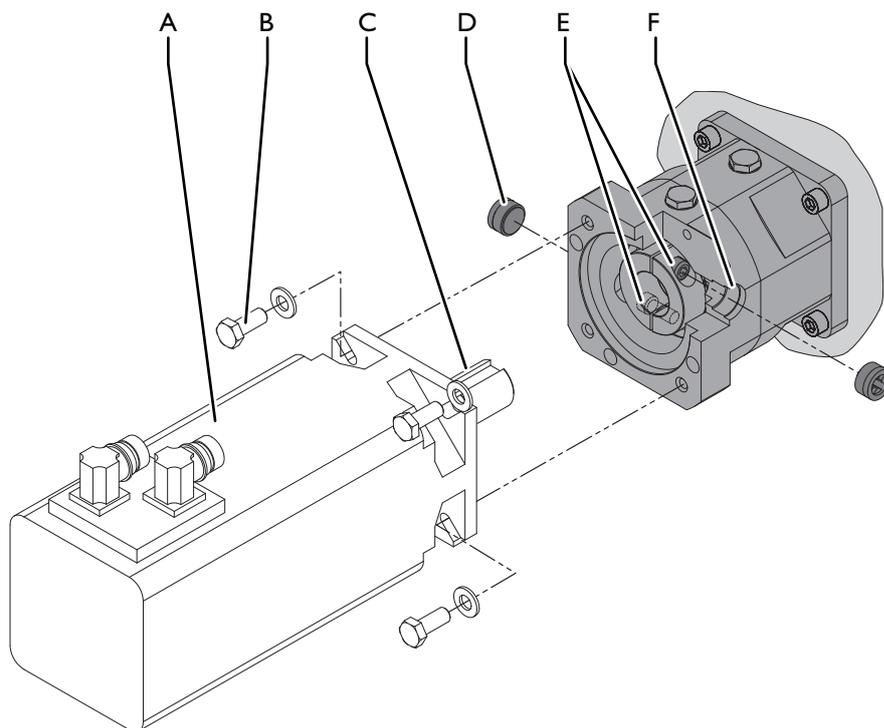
Удалить мотор: Планетарный редуктор Güdel
